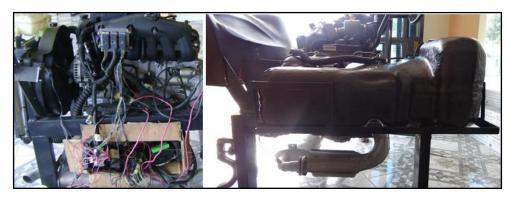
Ensamblaje de los componentes necesarios para el funcionamiento del motor
